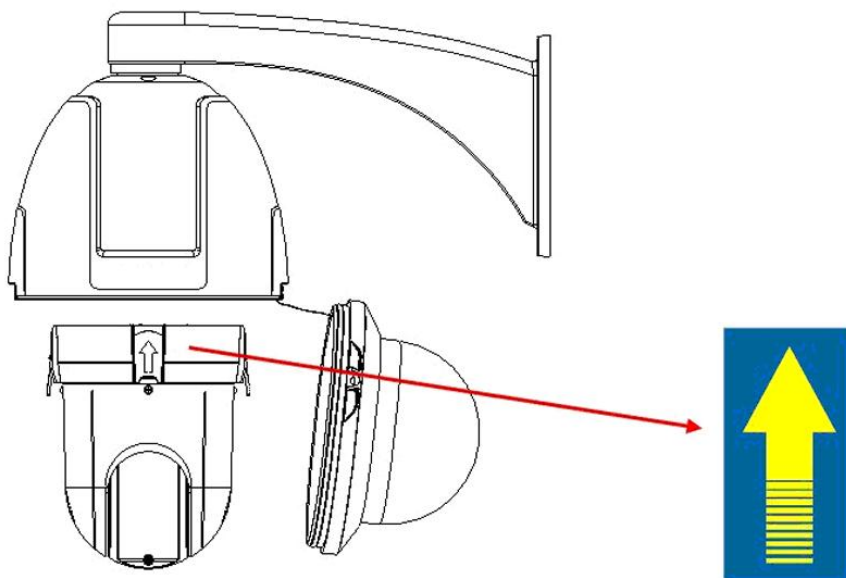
Installation du dispositif d'entraînement du dôme
